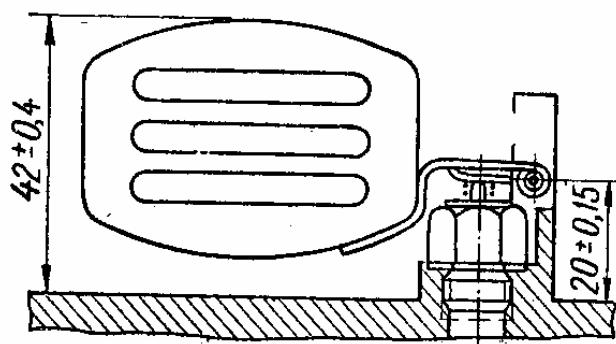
Схема розміщення поплавка в карбюраторі К-135МУ
